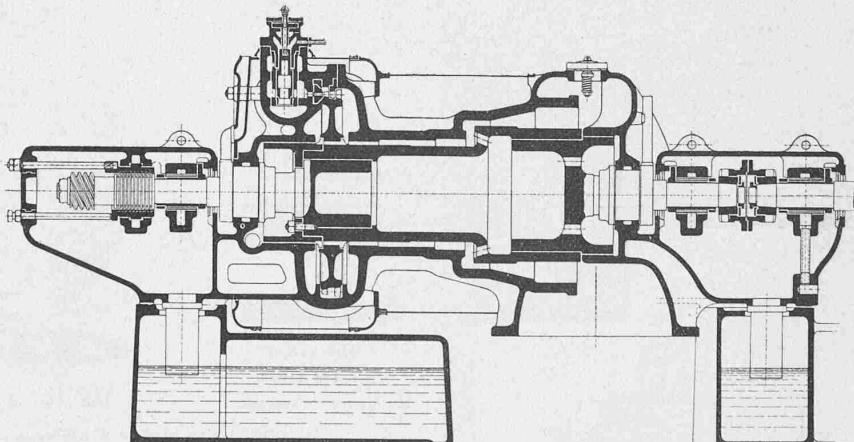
Dampfturbine nach Bauart Brown, Boveri & Cie., Baden. — Etwa 1:40.
